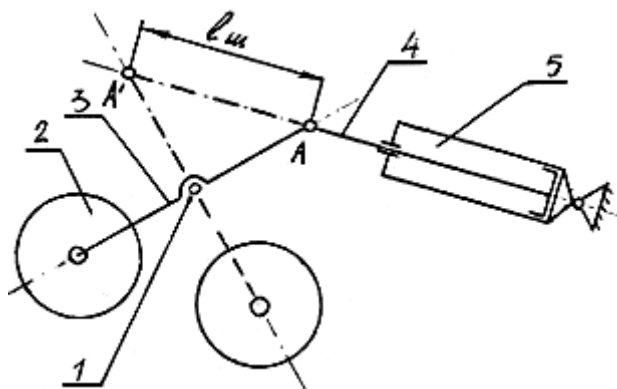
Схема к расчету перемещения штока механизма поворота крышки:
